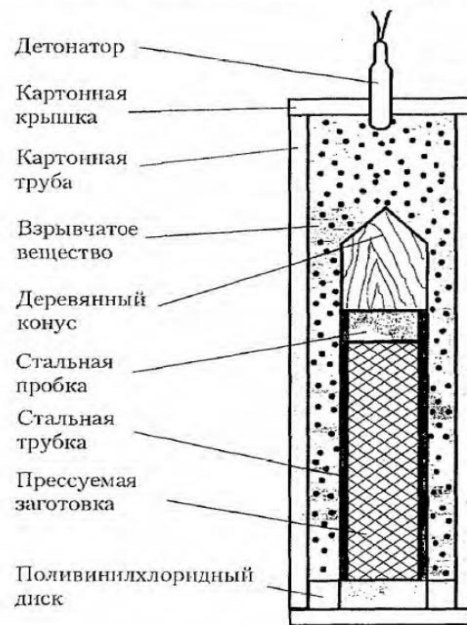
Схема получения цилиндрических композиционных материалов сваркой взрывом
